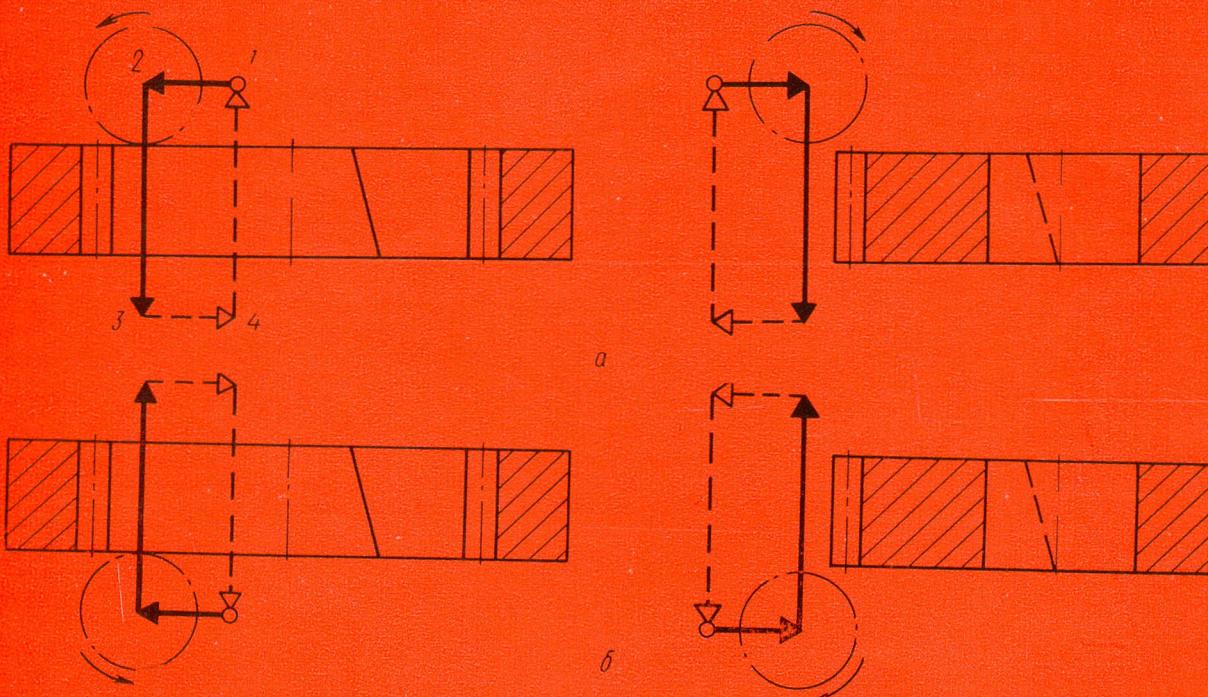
Схема движения дисковой фрезы при нарезании косозубых колес:
